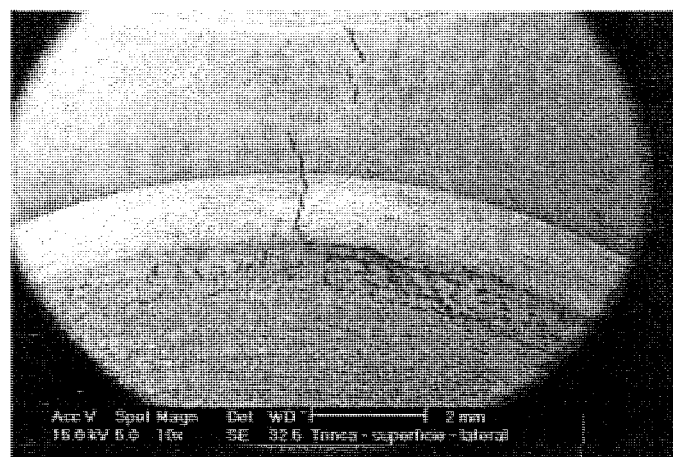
Outro aspecto de uma trinca unindo os rebaixos de usinagem, desta vez a trinca apresenta um caminho de propagação bem sinuoso. Verifica-se que a trinca propaga não só na superfície como também na parede lateral deixada pela usinagem. Material A após 17 ciclos térmicos com temperatura máxima de 500°C, corpo de prova com canto vivo de usinagem.
